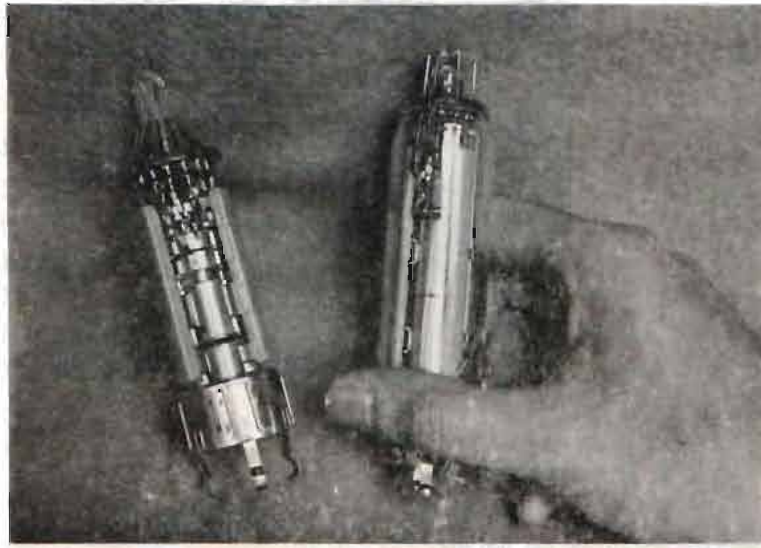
Acabado. Ensamblado y soldado de las últimas piezas. Colocado y cortado de funda de cristal.
